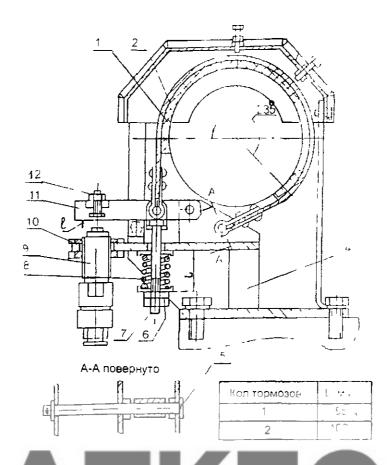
Тормоз грузовой лебедки 1 – накладка; 2 – лента; 3 - кожух; 4-кронштейн, 5-ось, 6, 10 – гайки; 7-тяга; 8 – пружина; 9 - гидроразмыкатель; 11 – рычаг, 12 - винт
